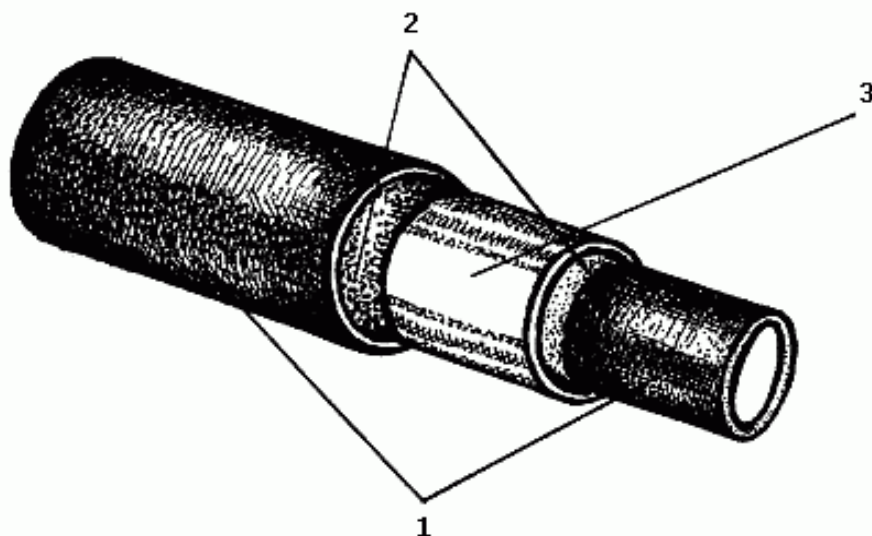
Металлополимерная труба: 1 – слой полиэтилена; 2 – связующий слой; 3 – алюминий
